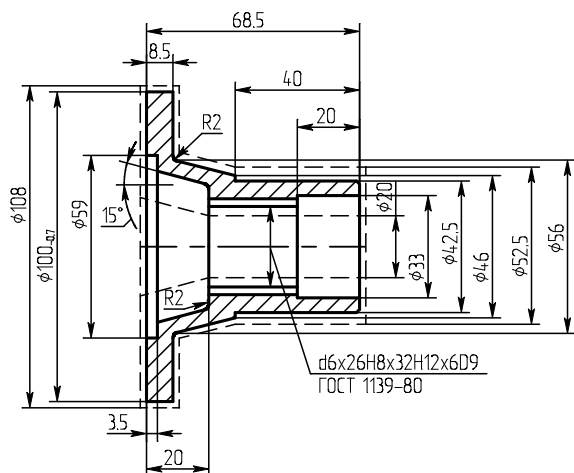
Чертеж детали фланца с втулочной частью (пунктиром показан контур поковки)
